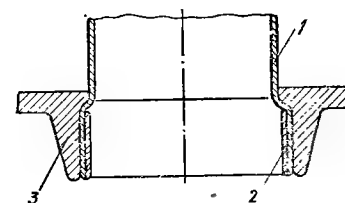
Рукав, открытый с двух сторон, с креплением самозаклинивающими кольцами:
